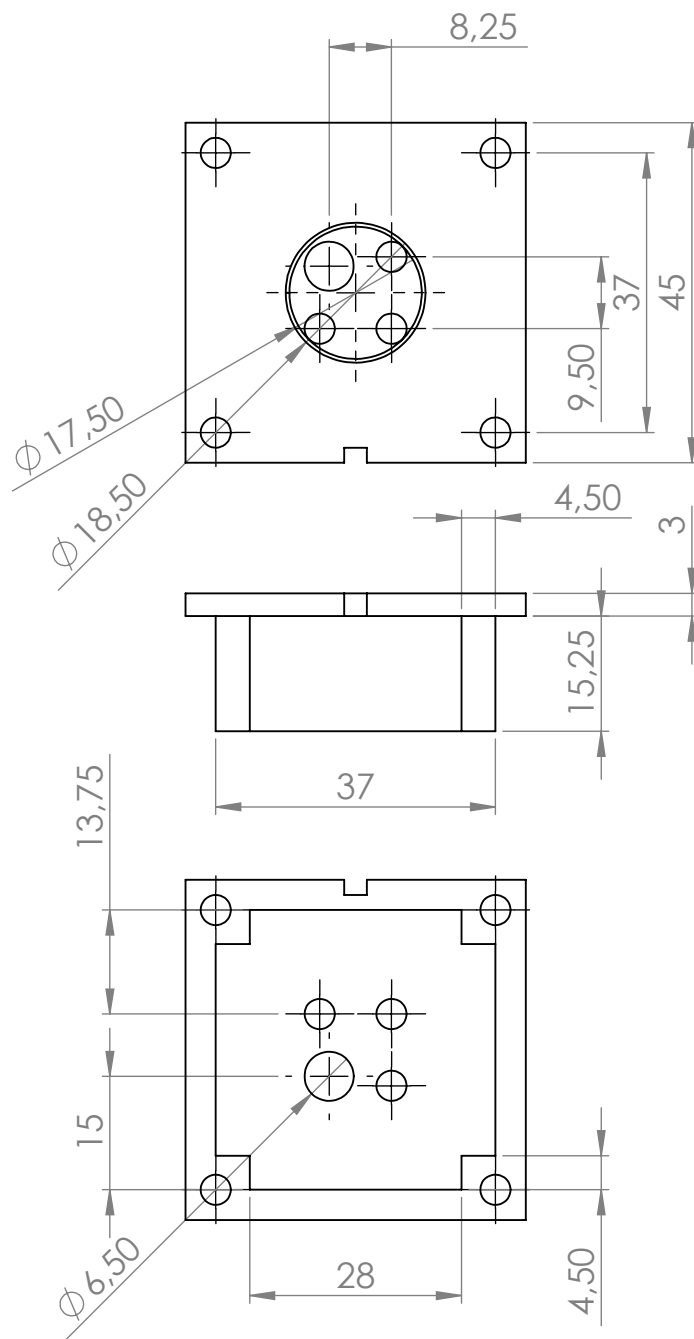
Diseño del molde para enmallado interno del *Robot Uniaxial* parte B
